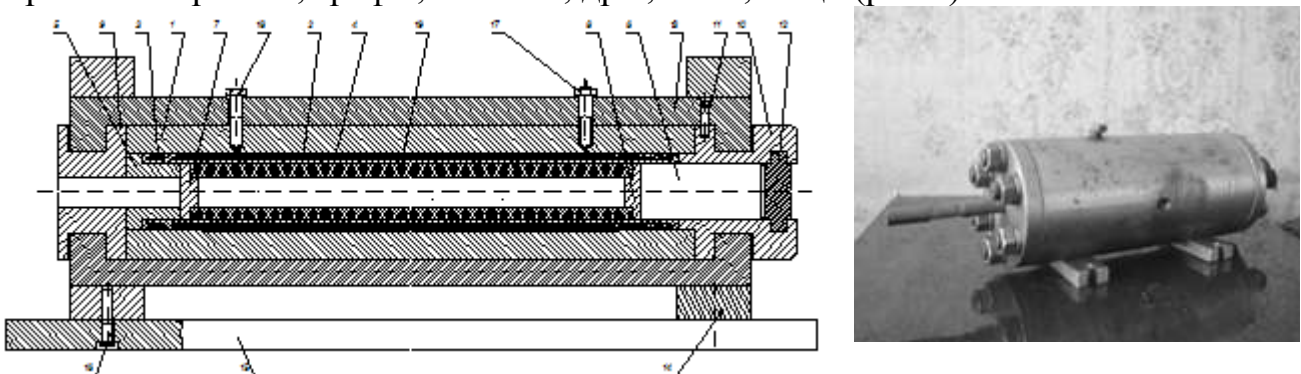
Пристрій для пресування ущільнювальних матеріалів різного роду: металічні, керамічні порошки, графіт, волокна, дріт, сітка, тощо: 1 – корпус; 2 – армована еластична оболонка з манжетами; 3 – вставки; 4 – робоча камера; 5-8 – проміжні упори; 9 – кільце; 10 – кришка; 11 – гвинт; 12 – повзун; 13 – жорстка циліндрична рама; 14 – кільце; 15 – стіл; 16 – гвинти; 17 – штуцер; 18 – заглушка; 19 – еластичний вкладиш
